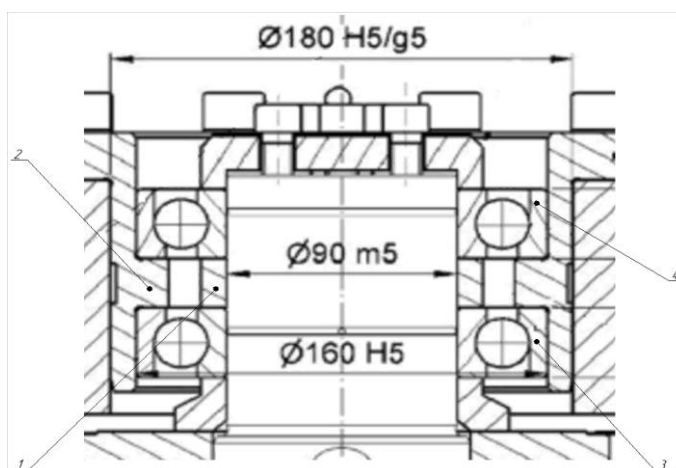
фрагмент чертежа редукторной части клетки до реконструкции
